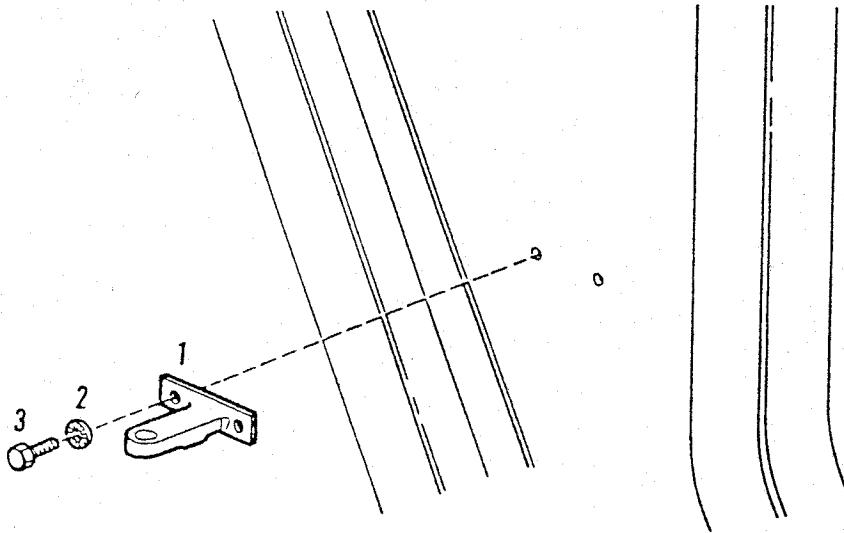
Befestigung des Montageteiles, Lautsprecher, im Fußraum vorne rechts
